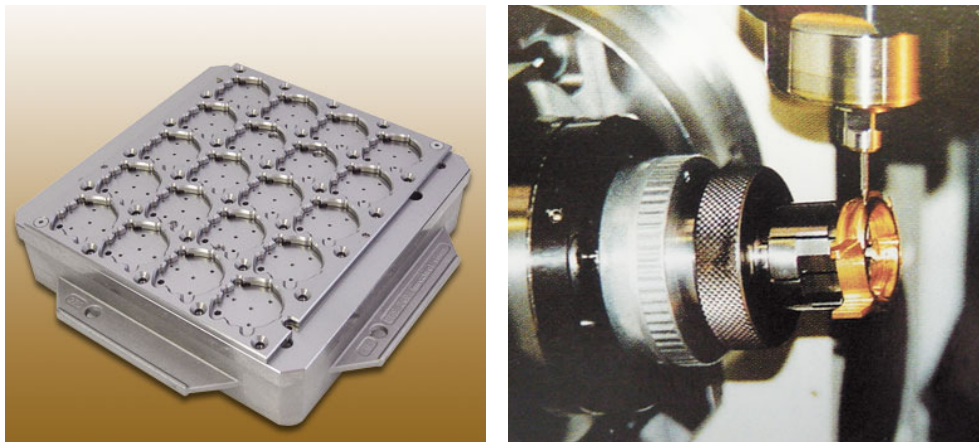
Primjena paletizacije u zrakoplovnoj industriji [21]
